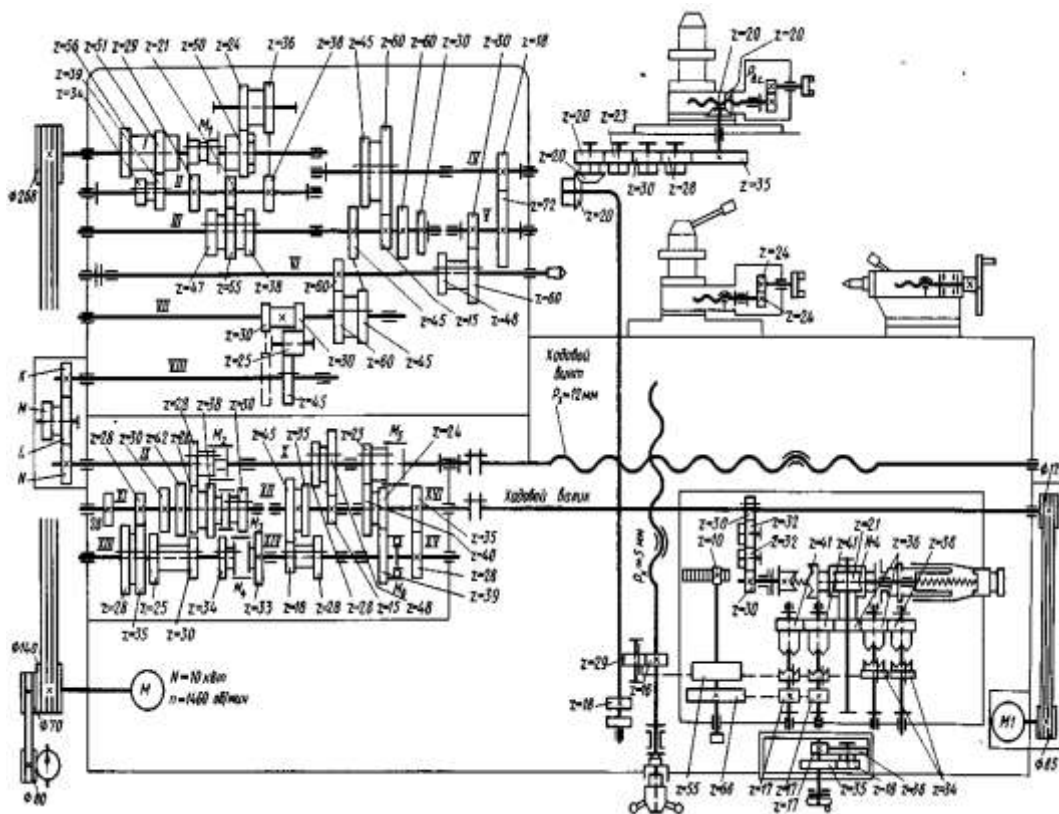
Кинематическая схема станка мод. 16K20, где: P.B.C. — шаг ходового винта верхнего суппорта; S B.C.— подача верхнего суппорта, мм/об.
